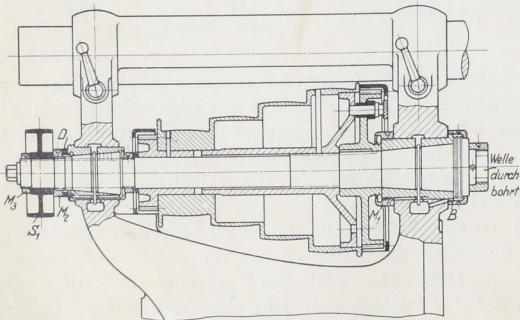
Spindelstock der Hendey-Norton Fräsmaschine. (Nach Hülle, Werkzeugmaschinen).
